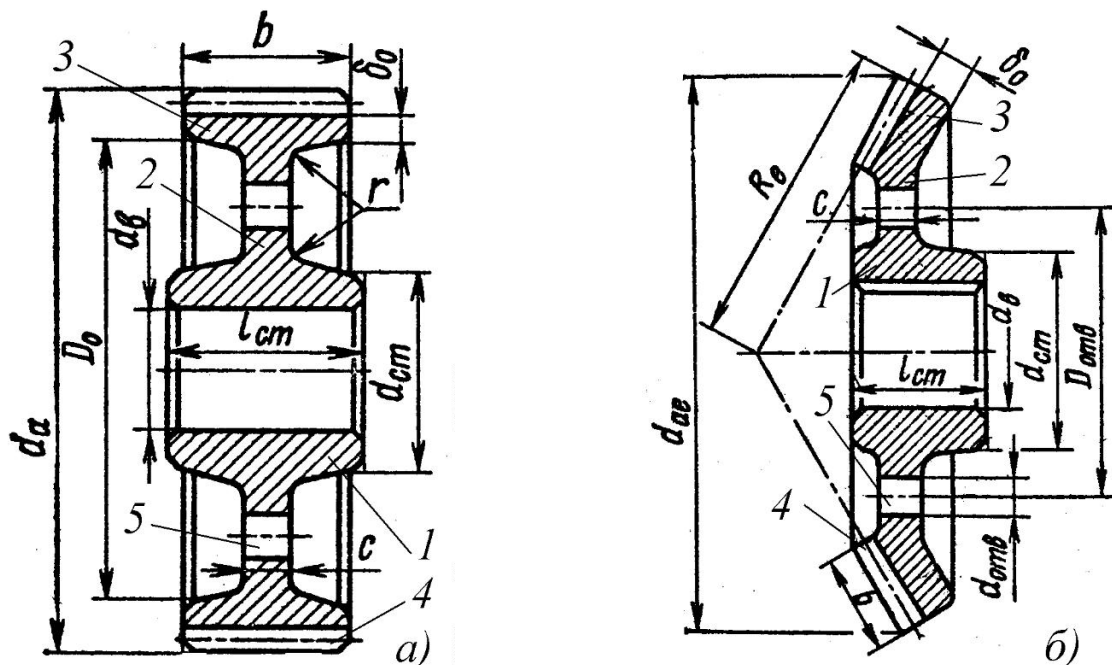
Конструкции цилиндрических (а) и конических (б) зубчатых колес
